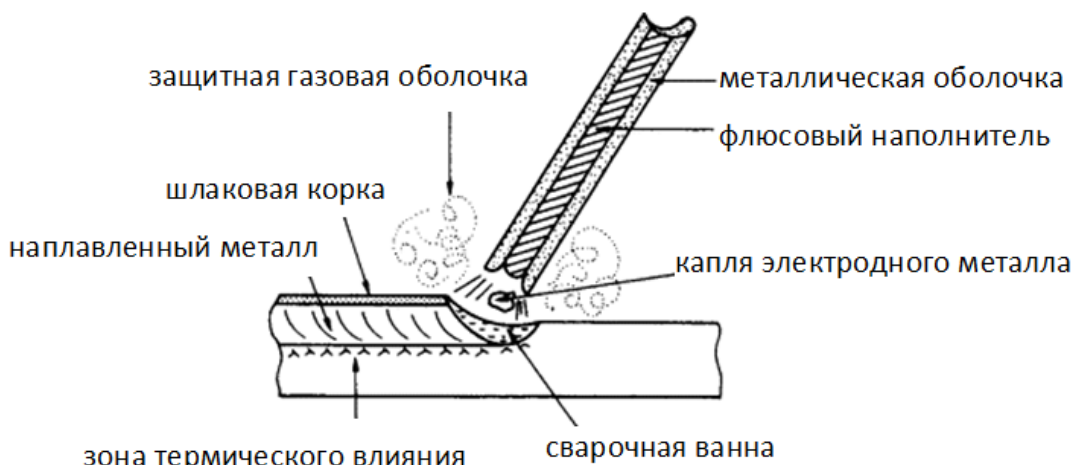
Схема сварки порошковой проволокой
